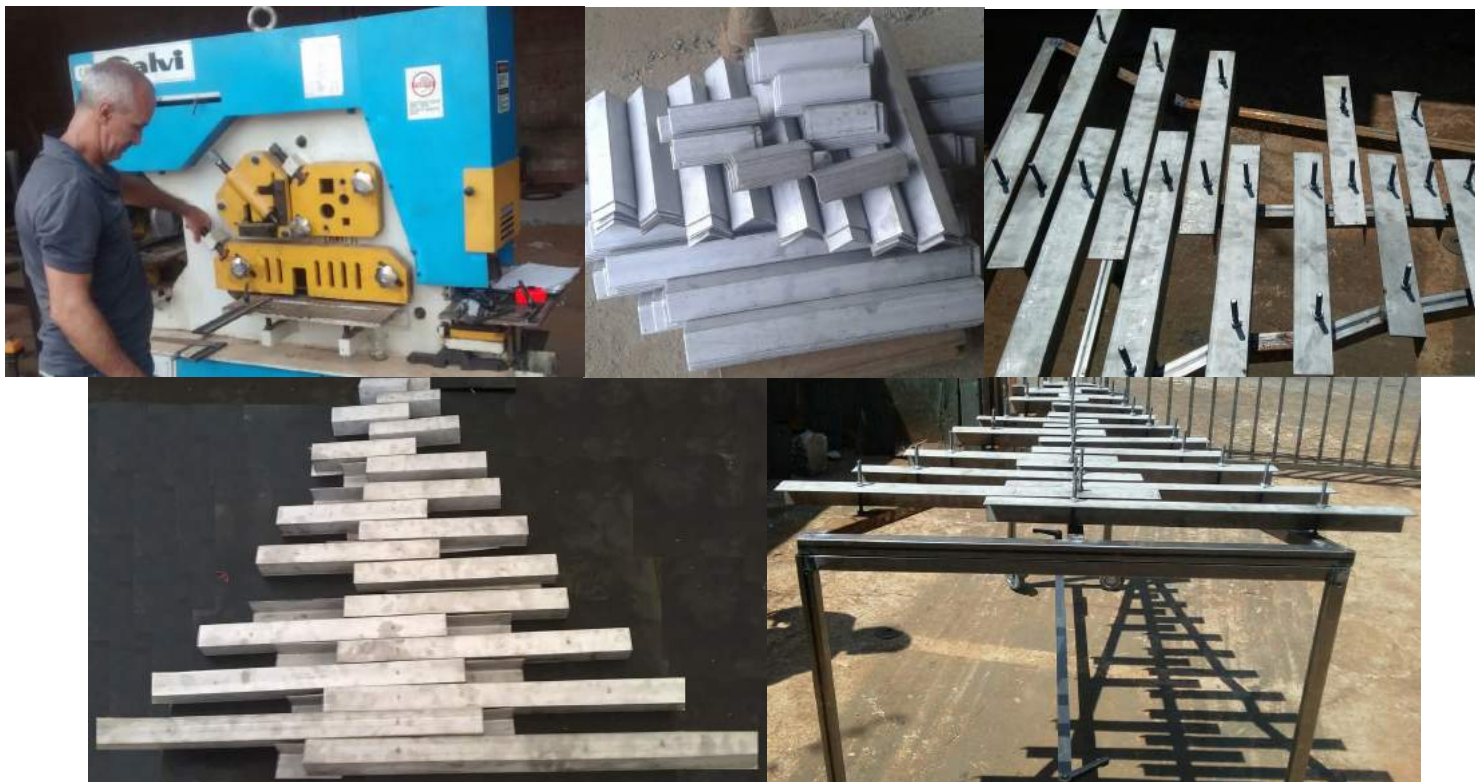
Sixsen final, detalhes das teclas em processo de corte, cortadas, em sua disposição geométrica e no teclado em construção.
